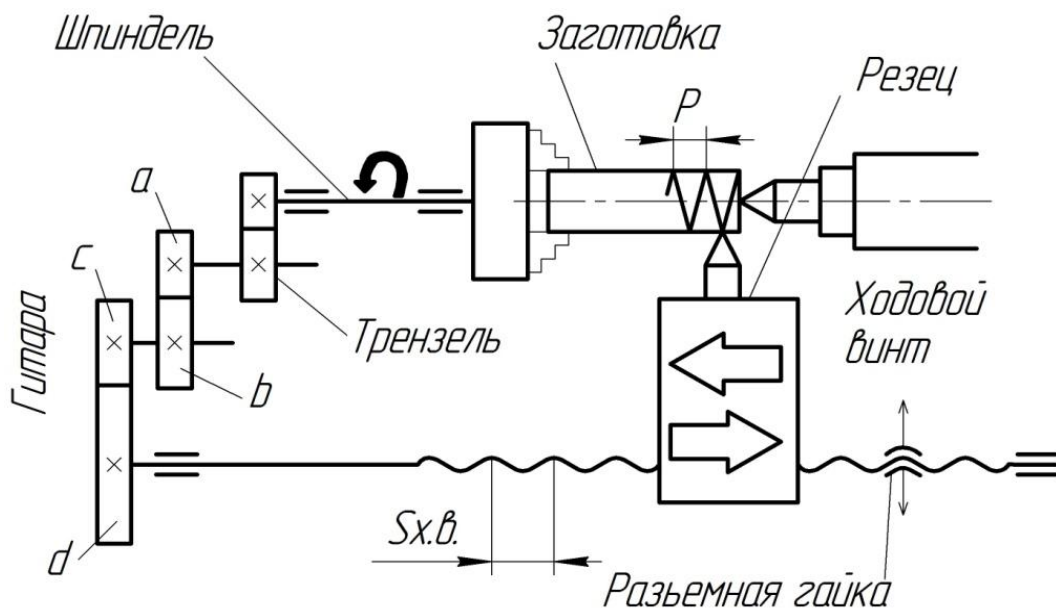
Схема настройки токарно-винторезного станка на нарезание резьбы
